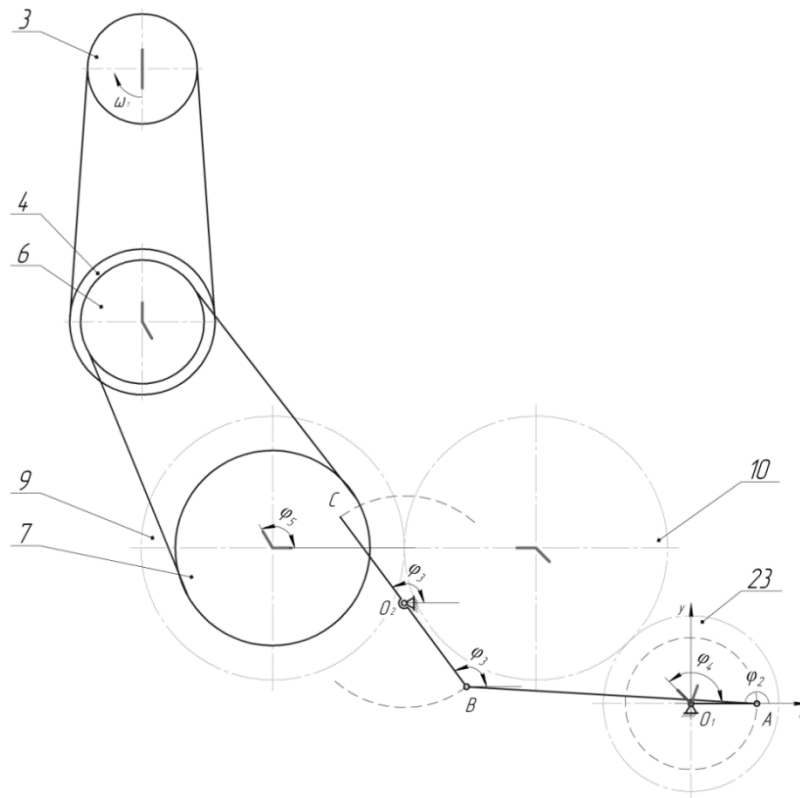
Кинематическая схема исполнительного механизма плетения (вид сверху)
